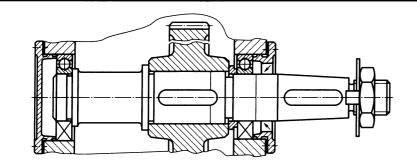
Выходной вал цилиндрического зубчатого редуктора
